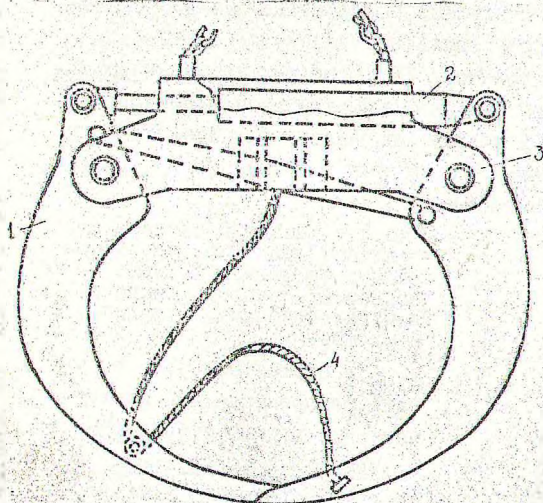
Клещевой захват трелевочного трактора: 1-челюсть; 2-гидроцилиндр; 3-корпус; 4-трос.
